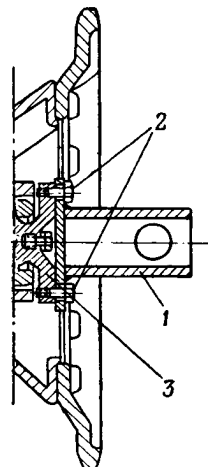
Ключ для выворачивания пробки ведущего колеса: 1 — ключ; 2 — стопорные болты; 3 — пробка.
